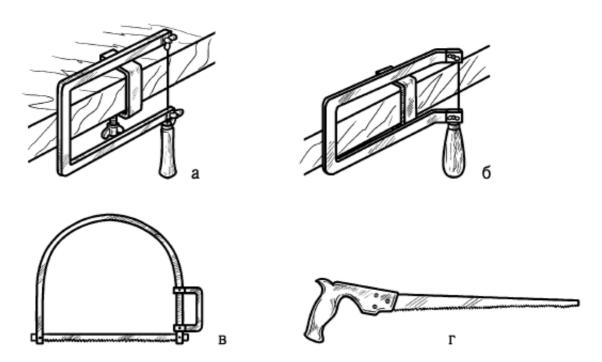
Инструмент для выпиливания: a – лобзик;  $\delta$  – лобзик с изогнутым станком;  $\epsilon$  – лучковая пила;  $\epsilon$  – выкружная ножовка
